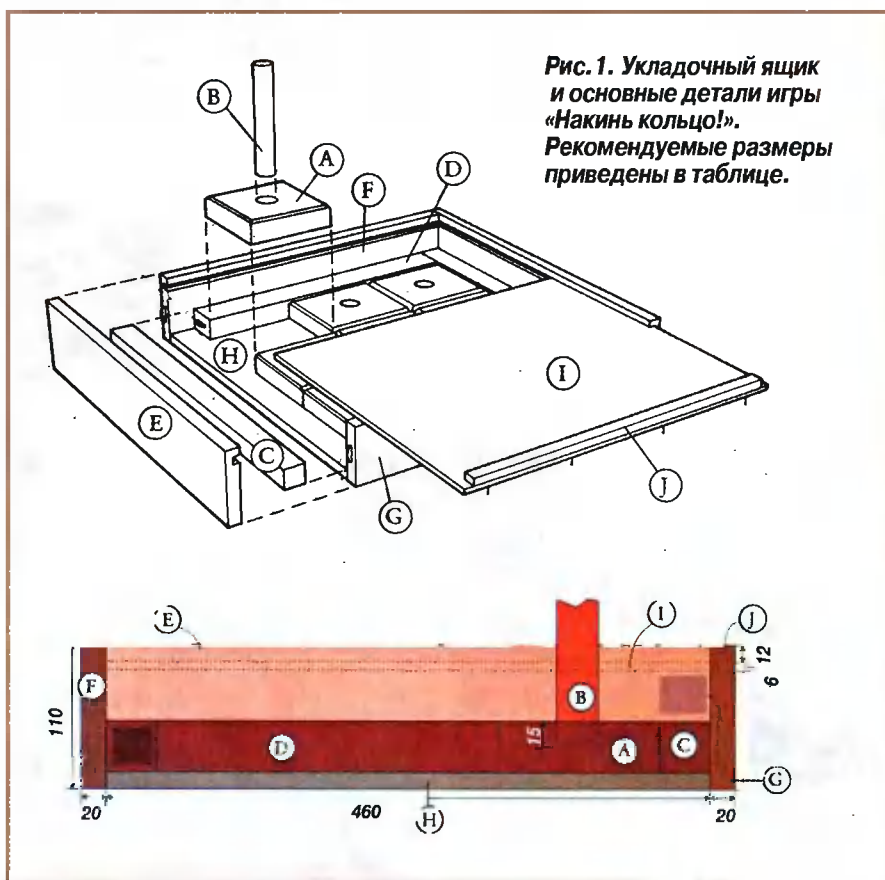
Укладочный ящик и основные детали игры «Накинь кольцо!». Рекомендуемые размеры приведены в таблице.
